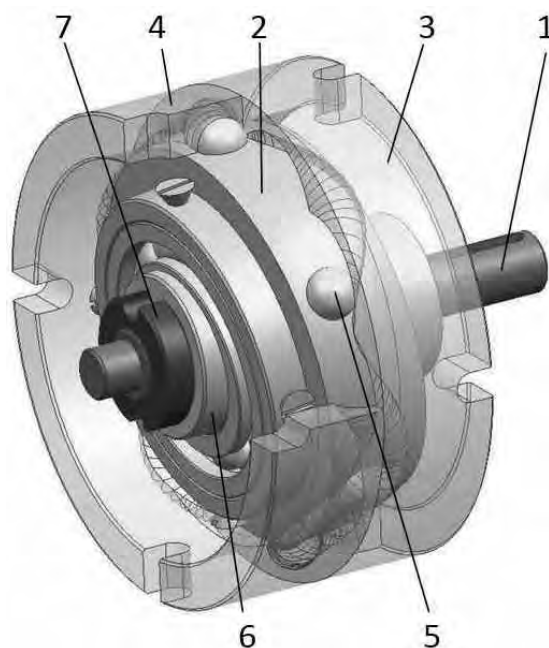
Конструктивная схема роликового зацепления: 1 – ведущий вал; 2 – генератор; 3 – левый наружный кулачок; 4 – правый наружный кулачок; 5 – ролик; 6 – косая шайба; 7 – гайка
